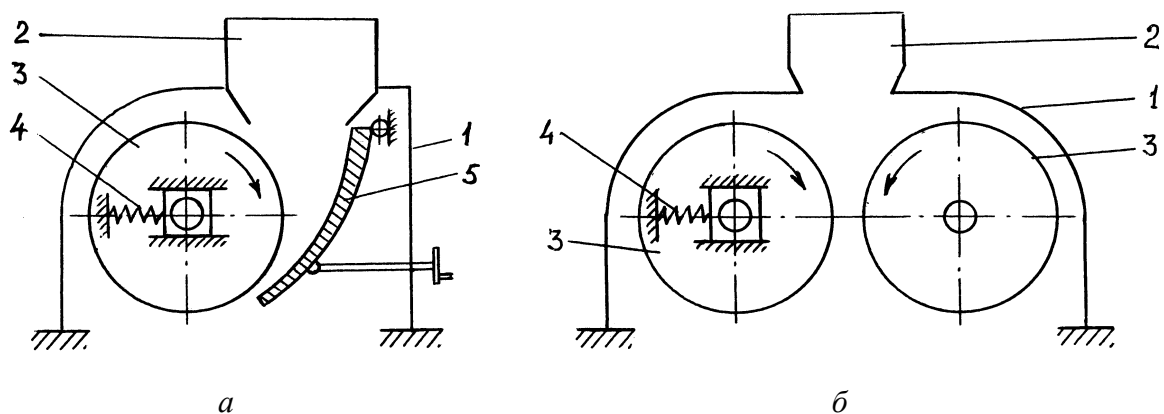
Схема валкових дробарок: а – одновалкової; б – двовалкової; 1 – корпус; 2 – завантажувальний бункер; 3 – валок; 4 – пружина; 5 – нерухома плита
